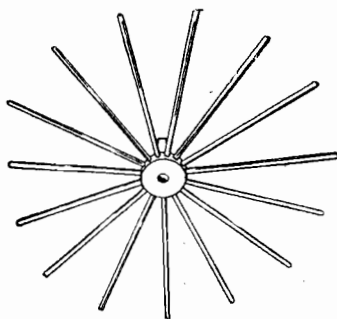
Supporto per l'avvolgimento di bobine a fondo di panier.
